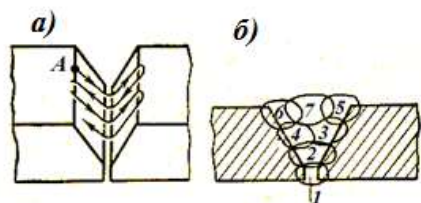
Сварка стыковых швов (шифрами обозначен рядок наложения слоёв шва)
